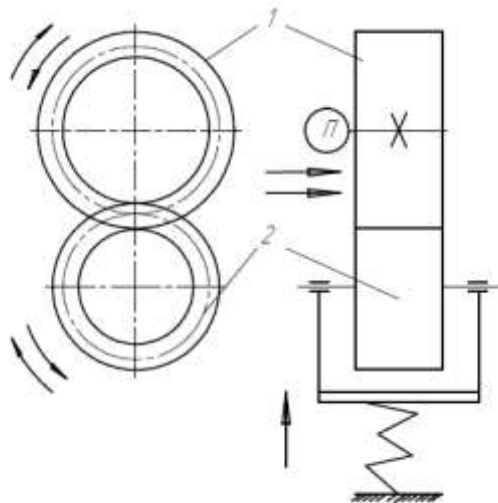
Базова кінематична схема зубохонінгування зубчастих коліс зубчатими дисковими хонами по пружній схемі.
